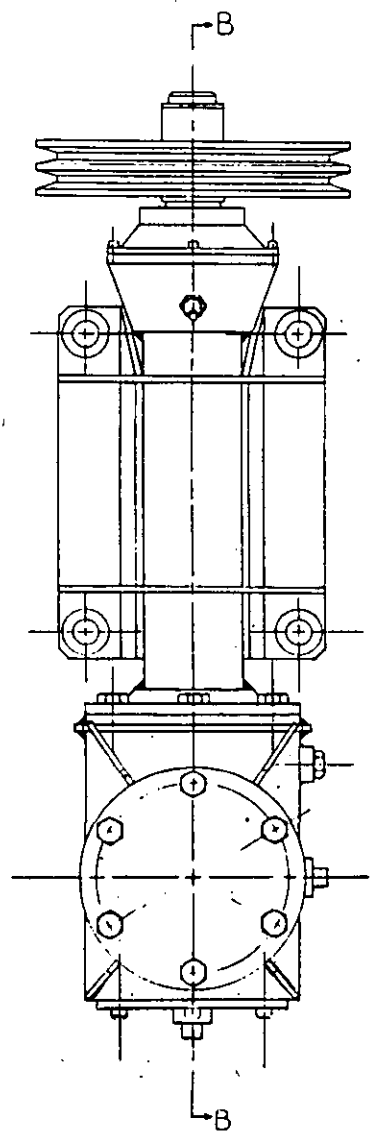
Dibujos del reductor con engranes cónico-rectos.
